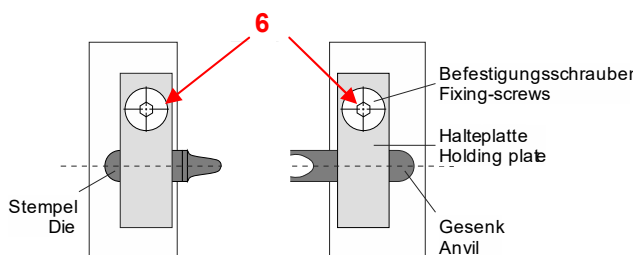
Crimpwerkzeug / Crimping tool
